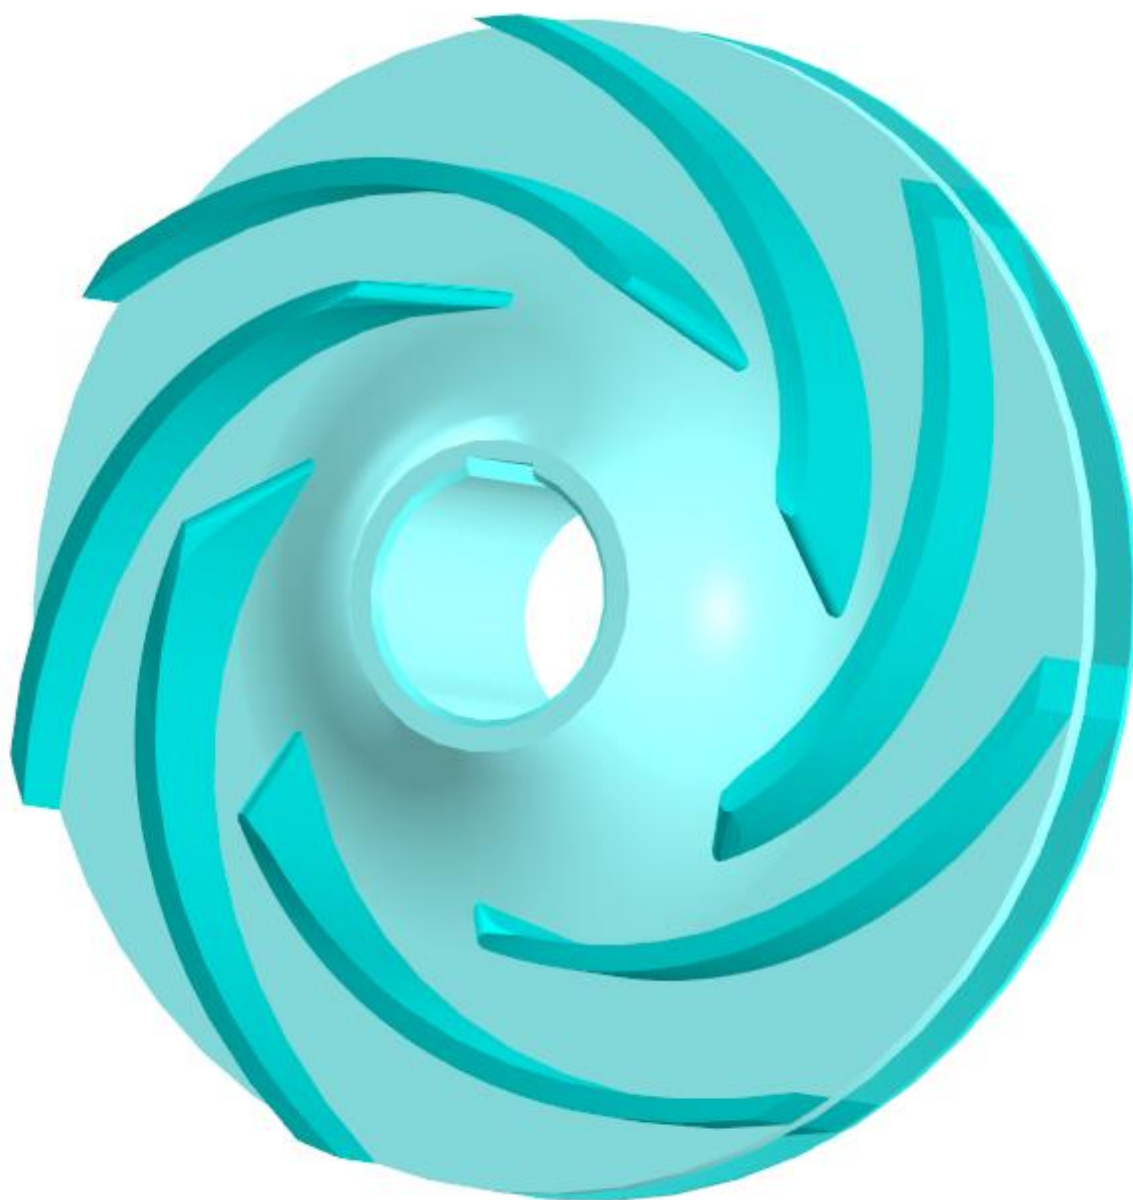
3D модель рабочего колеса без покрывного диска
